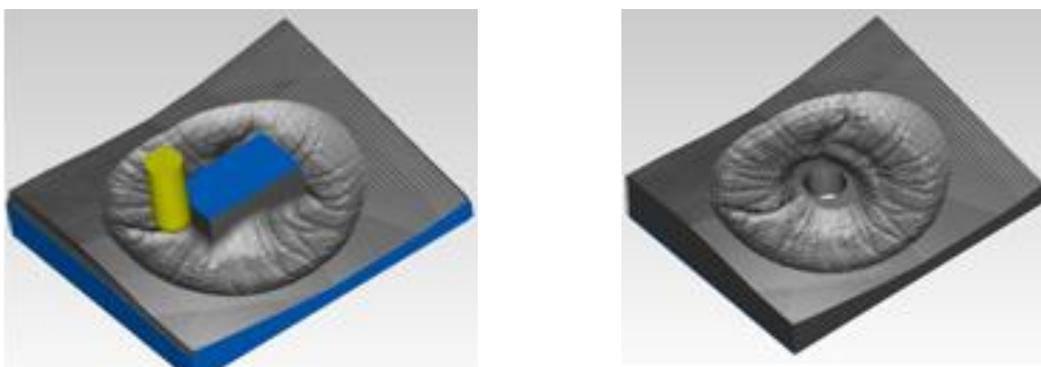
Процес фрезерування 3D слепка на станку з ЧПУ
